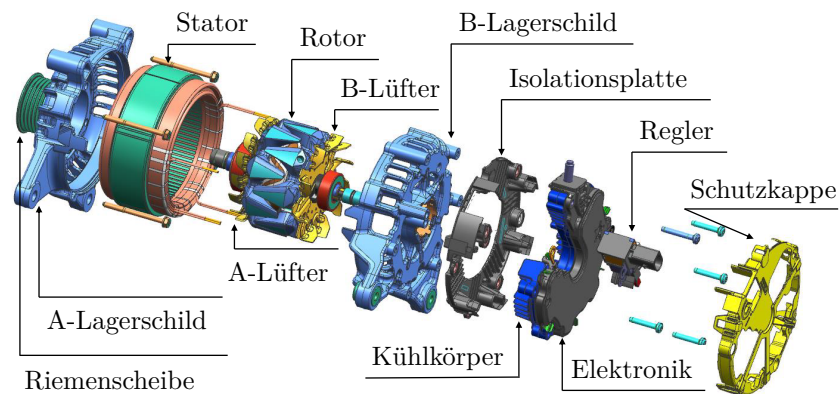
Explosionszeichnung eines SAR-Generators
